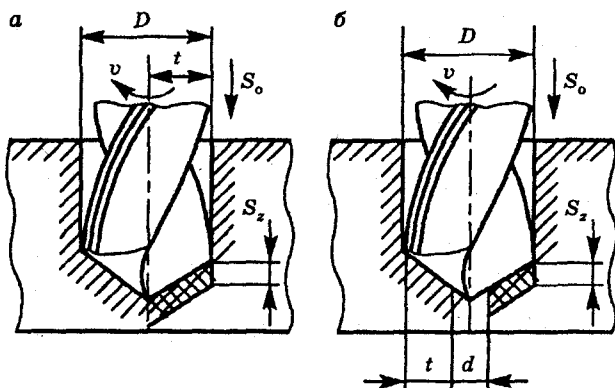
Схемы сверления (а) и рассверливания (б)
